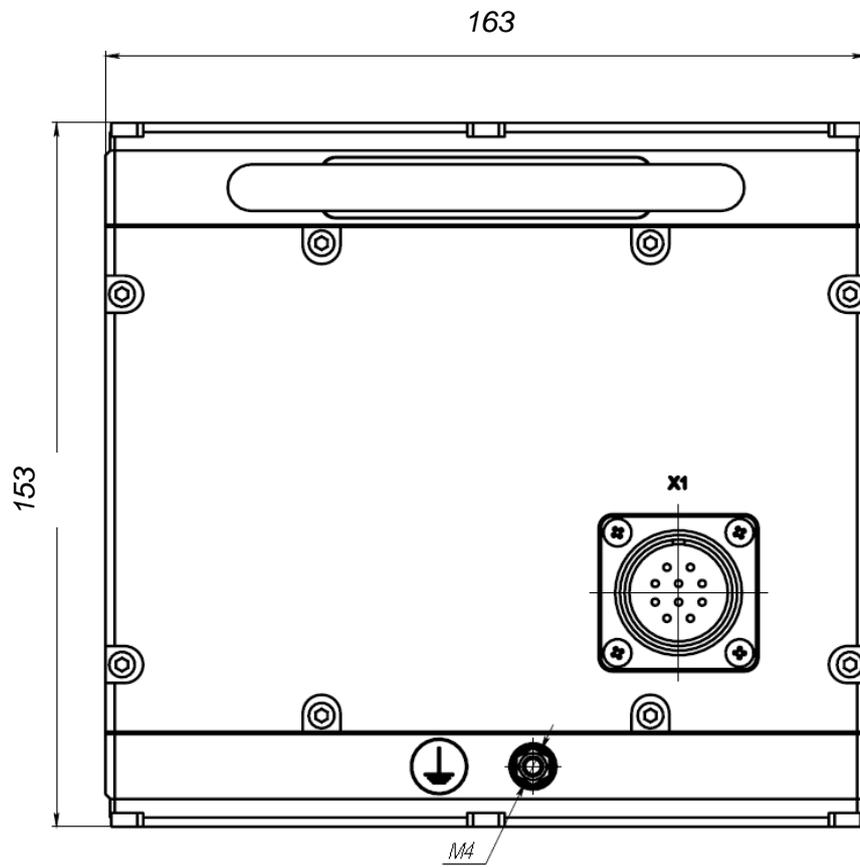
1 - Габаритные размеры ICC300 (вид спереди)
